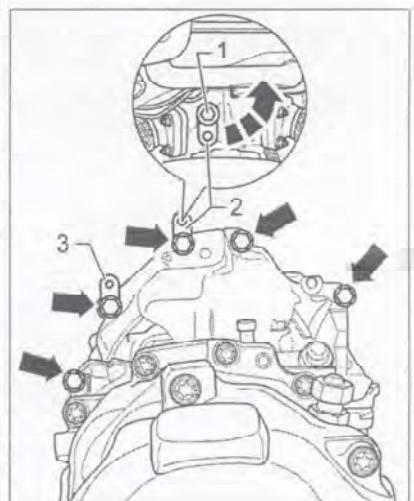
Отверните верхние болты крепления коробки передач к двигателю (стрелки).
